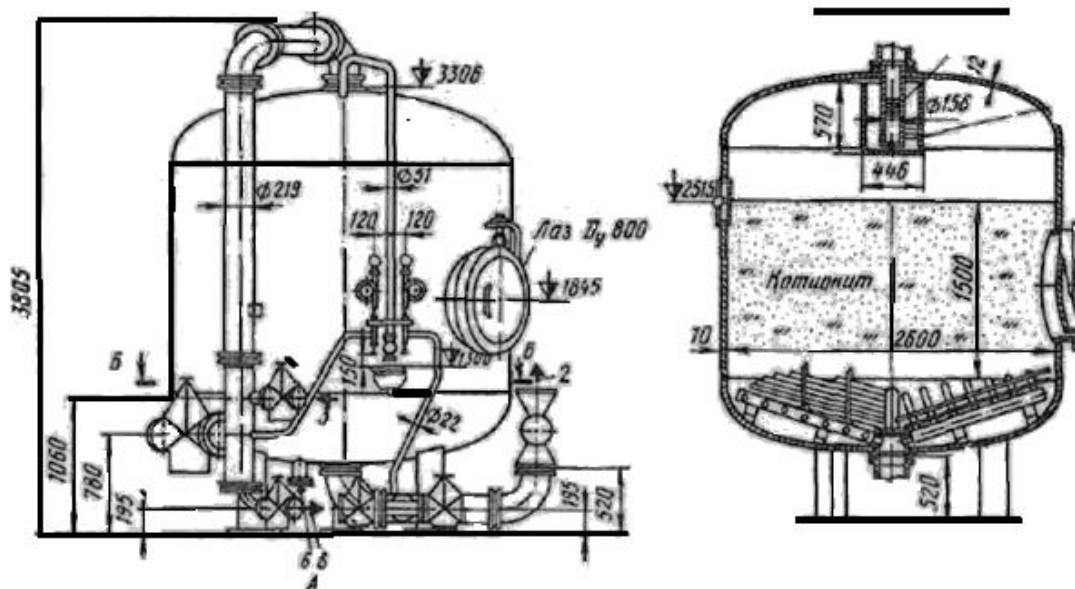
Фильтр ионитный параллельно-точный 2-й ступени ИПаП-2,6-0,6.
